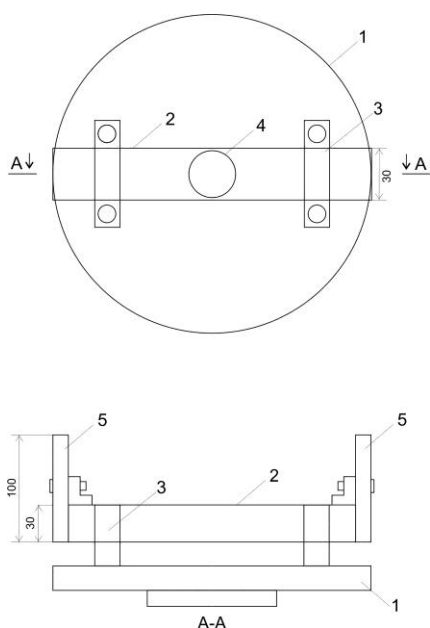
Схема лабораторного стенда с центробежным активатором
